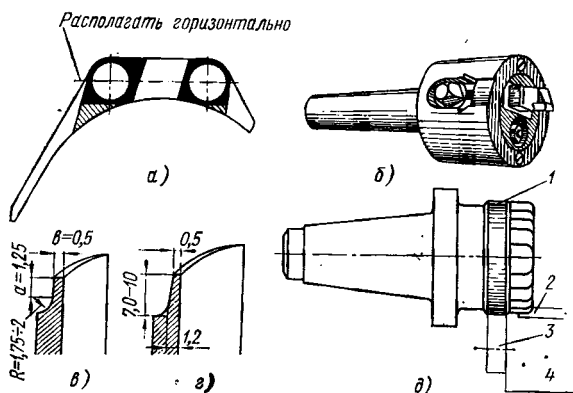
Формы шипов головок лопаток и инструменты для их обработки:
